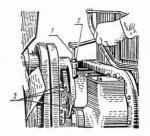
Регулировка натяжения ремней вентнлятора двигателей КДМ-46 и КДМ-100:
